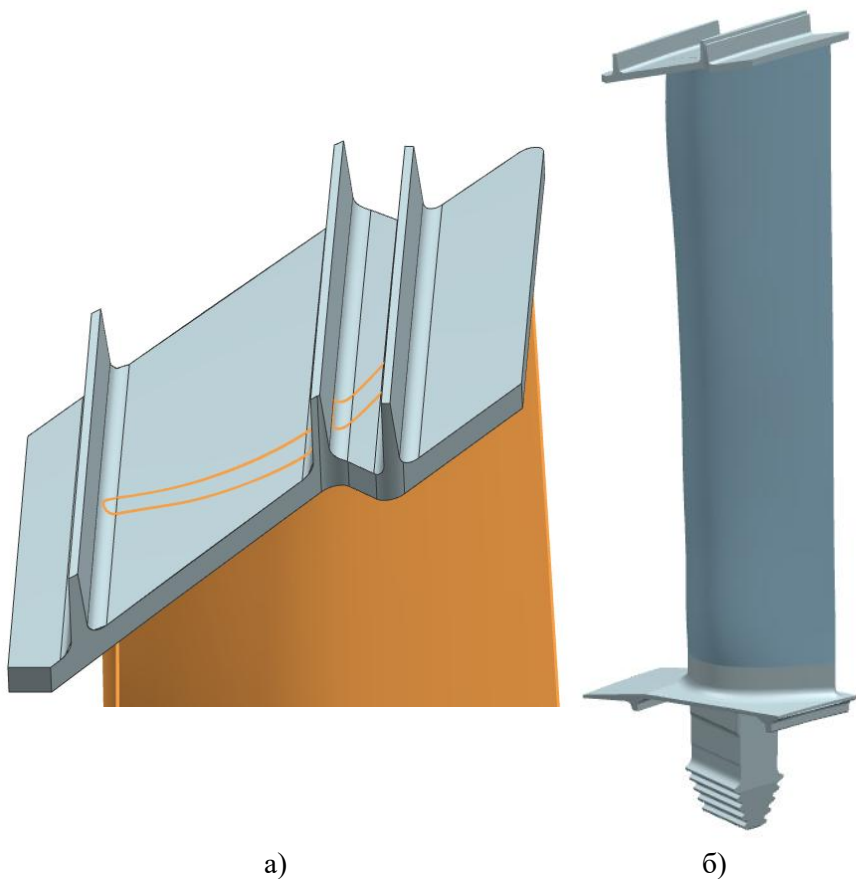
Параметрическая CAD 3D-модель рабочей лопатки турбины: а) бандажная полка, б) общий вид
